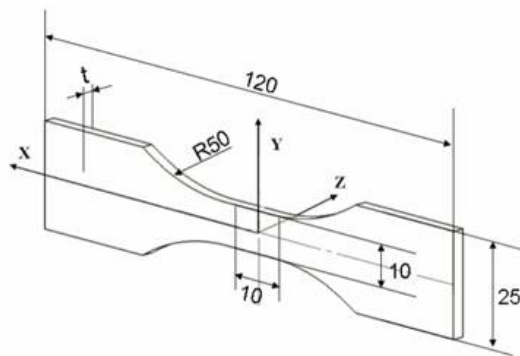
Dimensions de l'éprouvette utilisée pour les essais de fatigue
